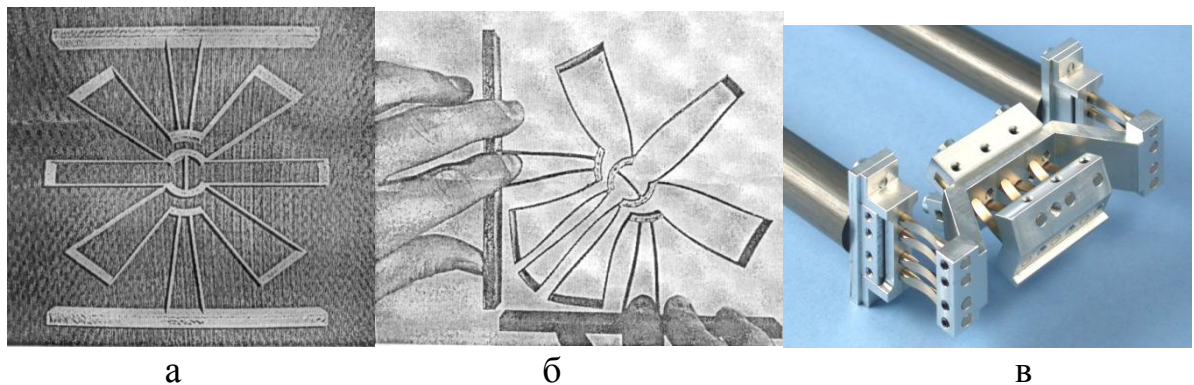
Конструкція одновісного пружного шарніра із фасонною пружиною (а), шарнір у деформованому стані (б) та пружний двохвісний шарнір із плоскими пружинами (в)
